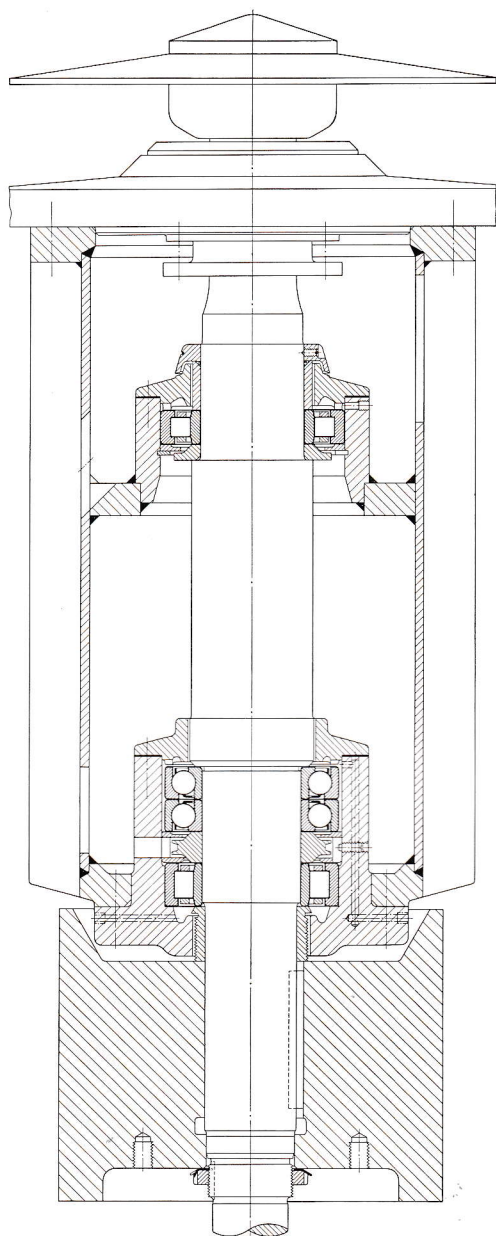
Disposición de rodamientos del eje de un desintegrador rápido
